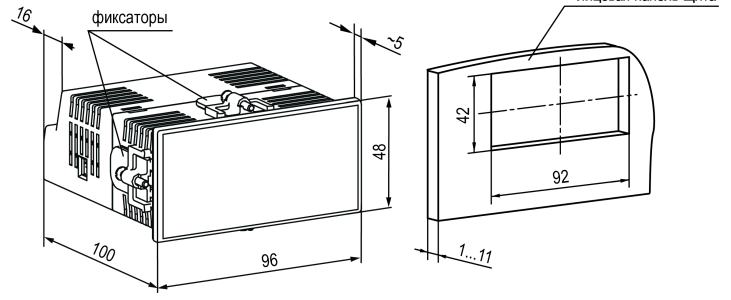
Габаритные размеры корпуса Щ2 и монтажного отверстия в щите
